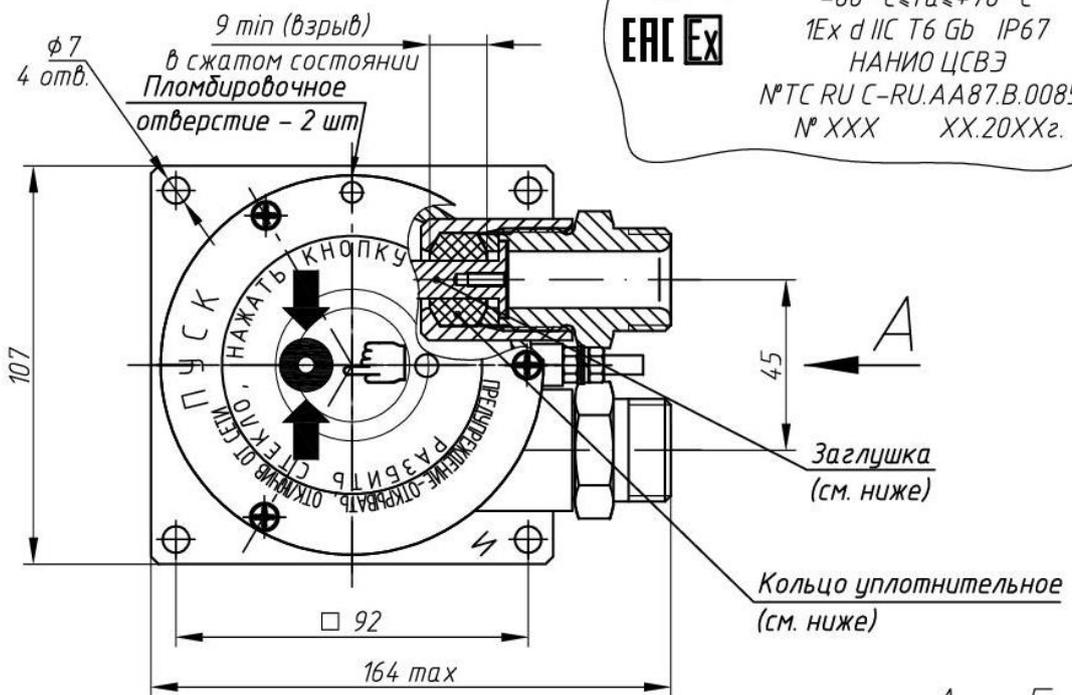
Габаритный чертёж ручных взрывозащищённых Извещателей ExIIP535-1B в корпусе из алюминиевого сплава, совмещённый с чертежом взрывозащиты. Монтаж кабеля диаметром от 8 до 18 мм.
